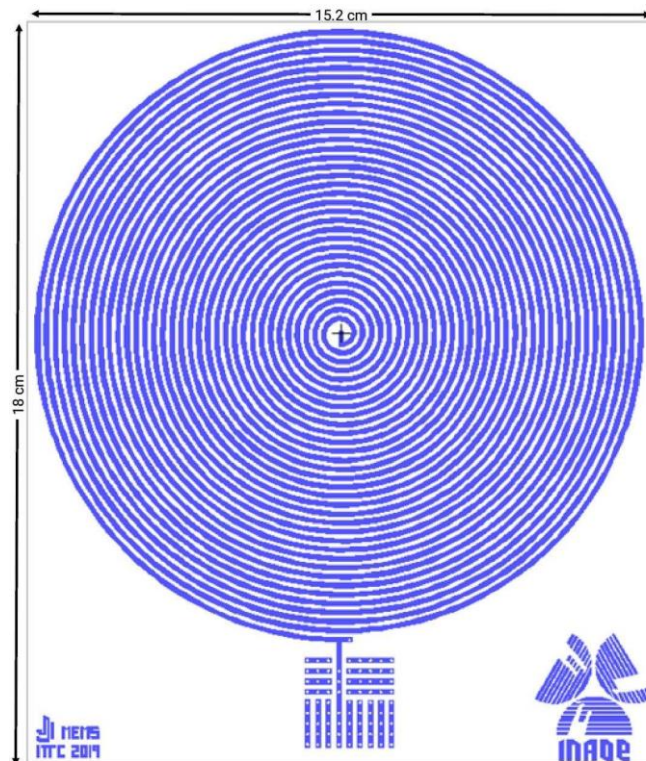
Diseño del patrón geométrico de la bobina transmisora sobre una placa de PCB.
